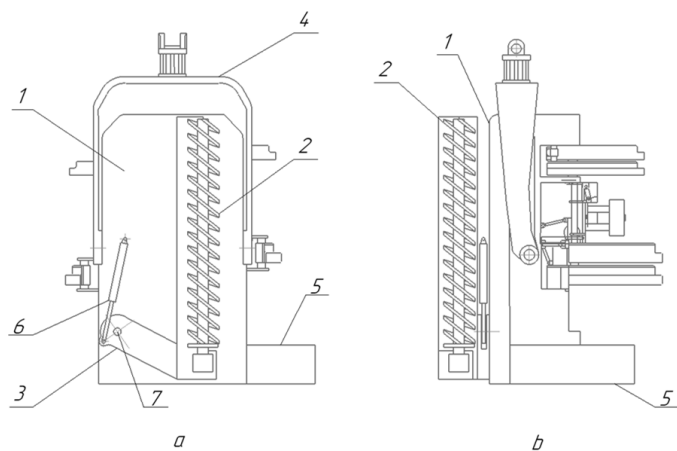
Модернизированная харвестерная головка в транспортном положении: а – вид сзади; б – вид сбоку
